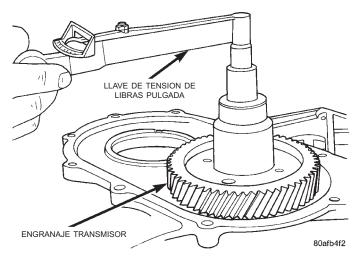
Verificación del par de rotación de los cojinetes del engranaje transmisor
